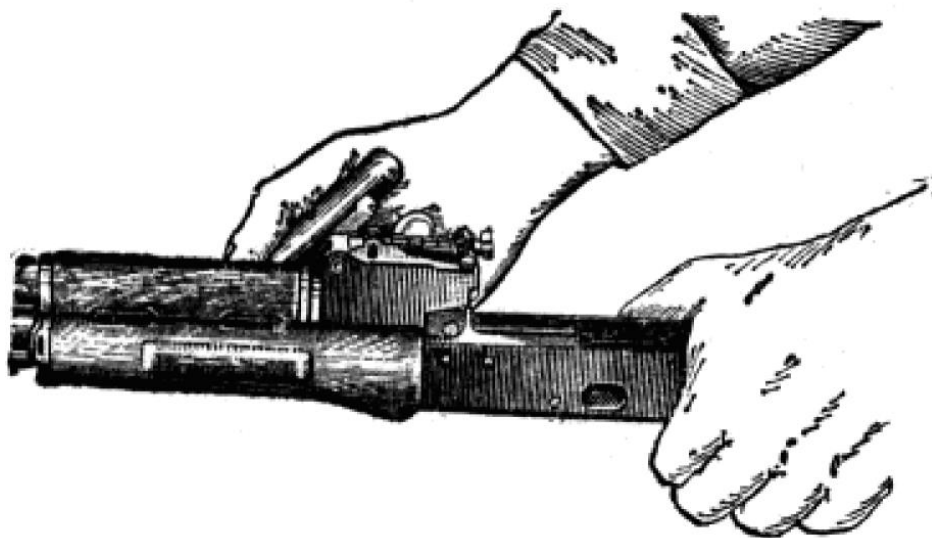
Поворот замыкателя газовой трубки с помощью пенала с принадлежностью
